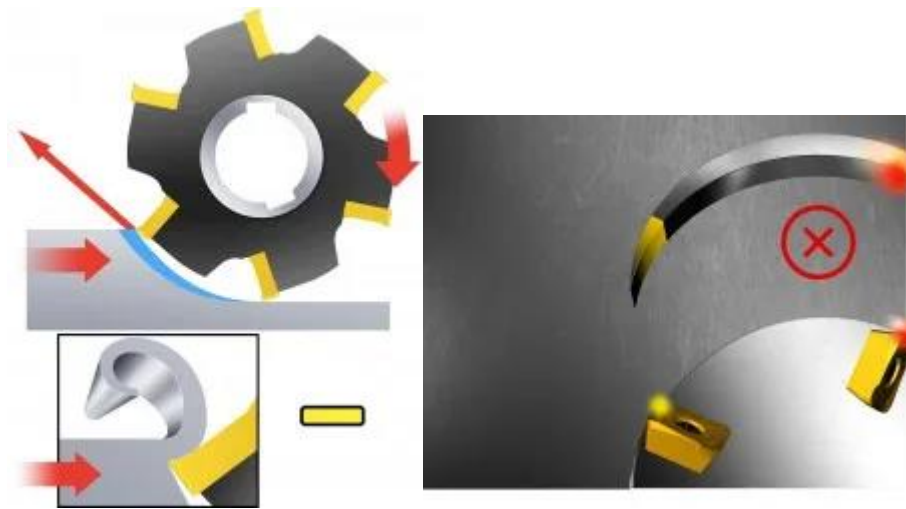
Зустрічне фрезерування, утворення стружки [18]
